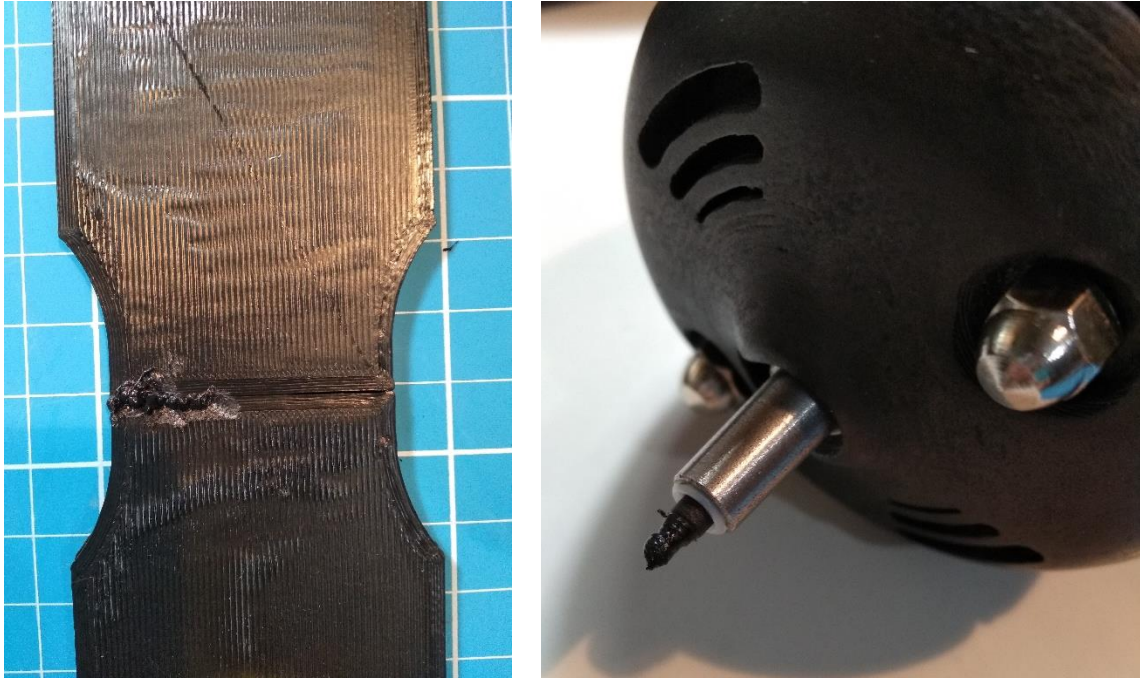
(Izquierda) soldadura con alta velocidad de avance 60 mm/min. (Derecha) Estado de la herramienta cuando el ángulo de inclinación de la herramienta es menor a 60° respecto la horizontal.
